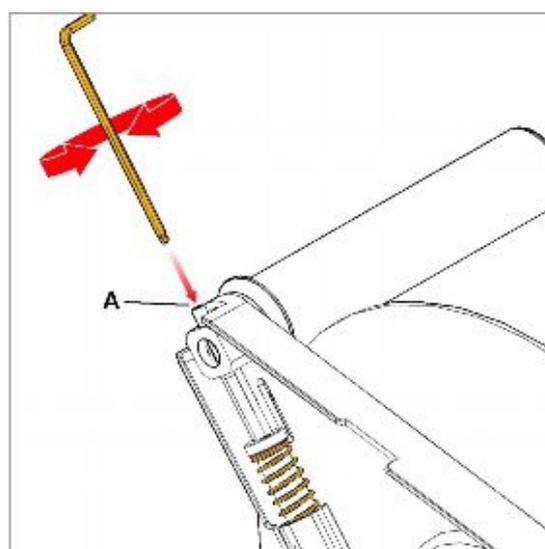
Регулировка силы восстановления пружины плавающего рычага на 300-мм размотчике
